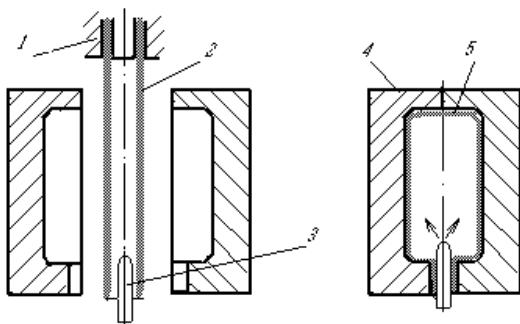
Общий вид экструзионно-раздувного агрегата
